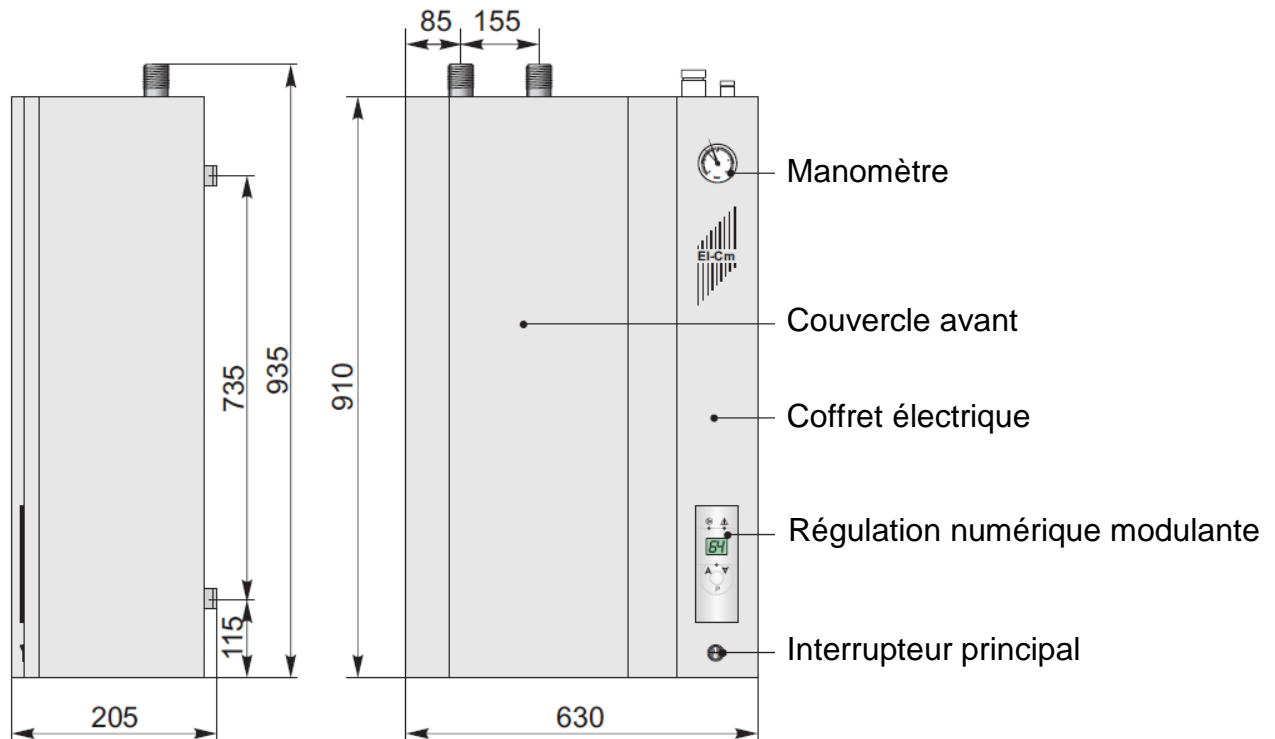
Dimensions techniques de base de la chaudière électrique ELECTRA CC
